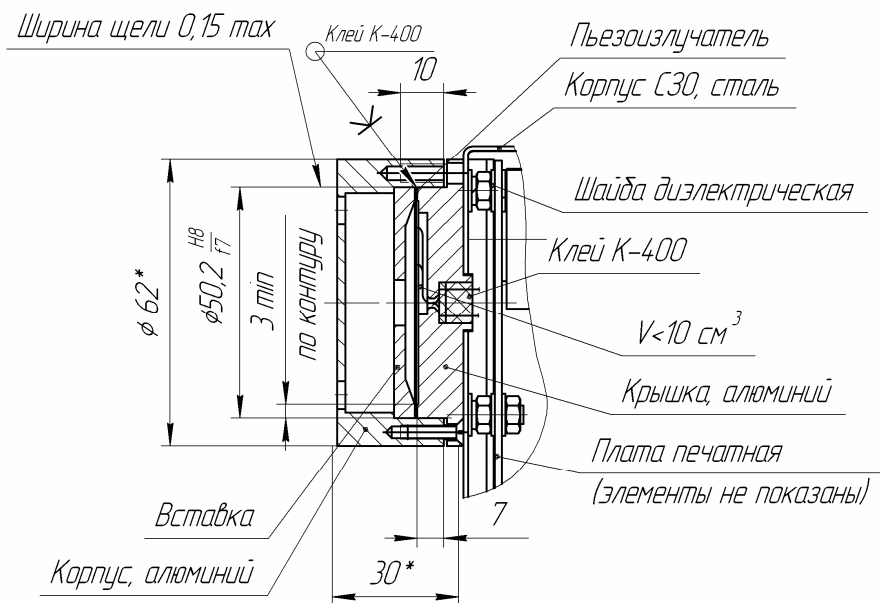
Звуковой излучатель с элементами конструкции, обеспечивающими взрывозащиту светозвукового оповещателя «СЗО-Фотон»
